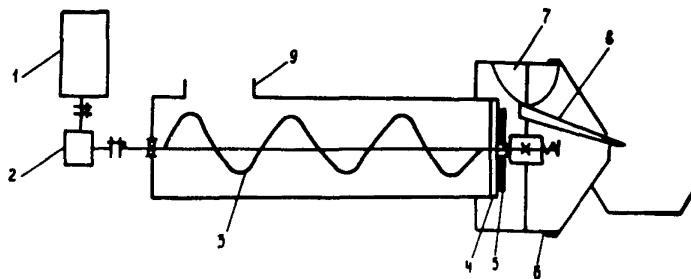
Кинематическая схема гранулятора киров; 1-электродвигатель; 2-редуктор; 3-шнек; 4-решетка; 5-нож; 6-барабан; 7-лопатка; 8-желоб; 9-загрузочная воронка
